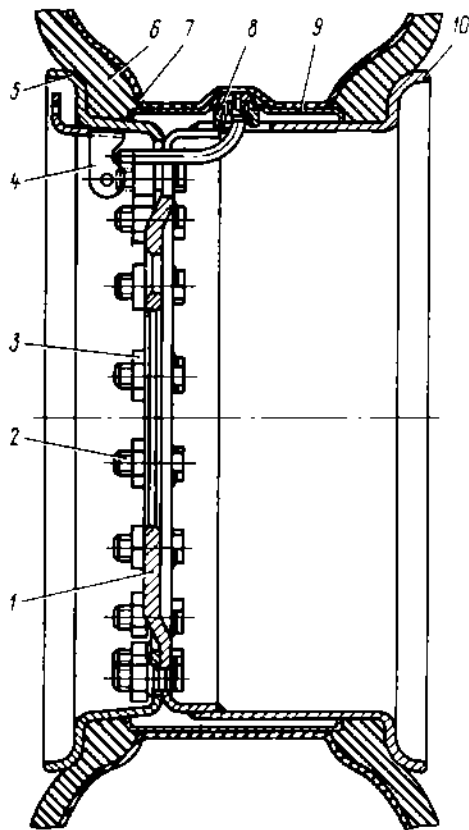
Колесо в сборе автомобиля ЗИЛ-157К:
